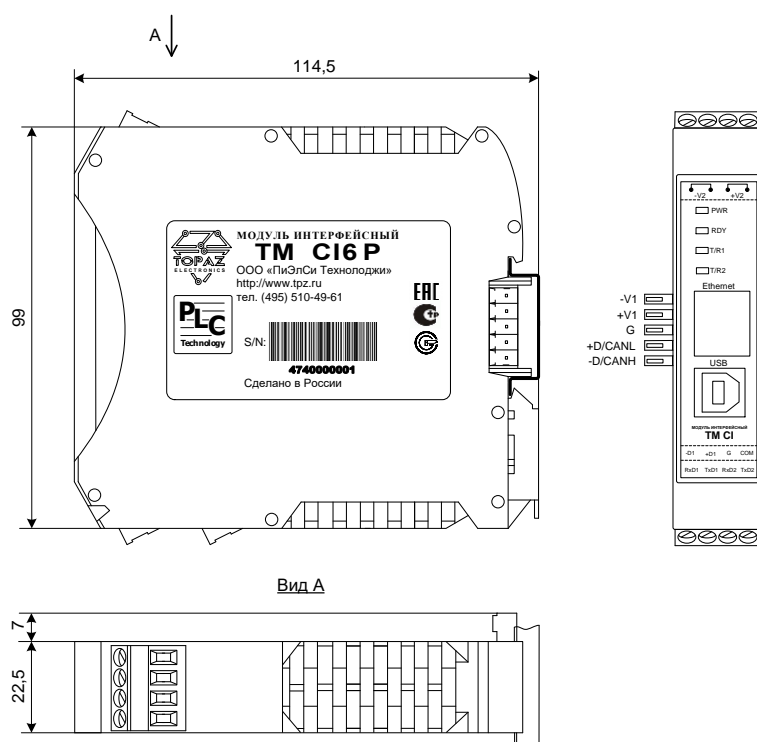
Внешний вид и габаритные размеры преобразователя
